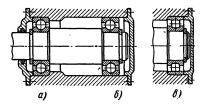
Установка горизонтального вала на двух радиальных шарикоподшипниках: а— закрепленый шарикоподшипник; 6— плавающий шарикоподшипник; 6— вариант плавающей опоры с роликовым подшипникм
